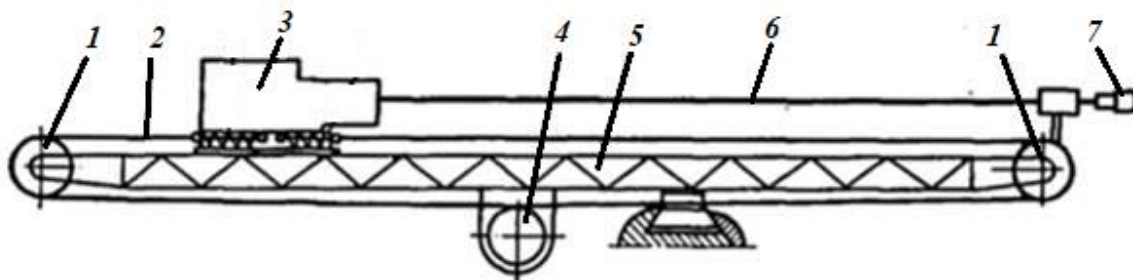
Схема канатного привода подачи: 1 – блоки; 2 – канат; 3 – привод вращения; 4 – барабан; 5 – направляющая; 6 – буровой став; 7 – исполнительный орган
